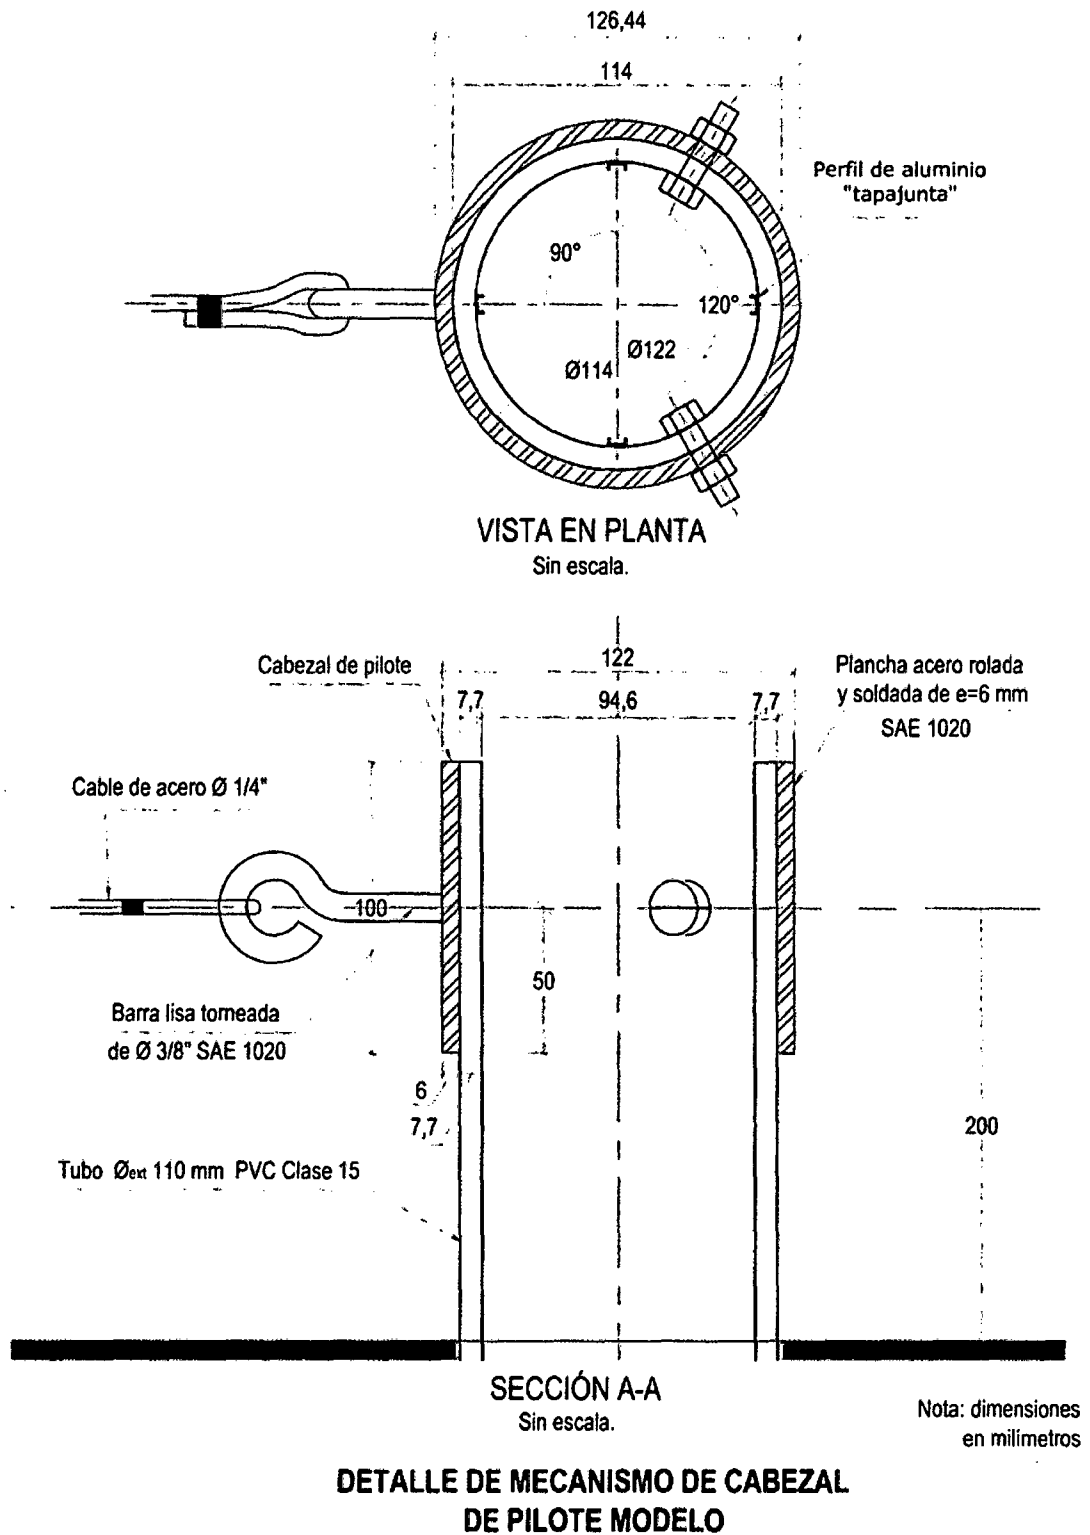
Detalle de mecanismo de cabezal de pilote modelo.
